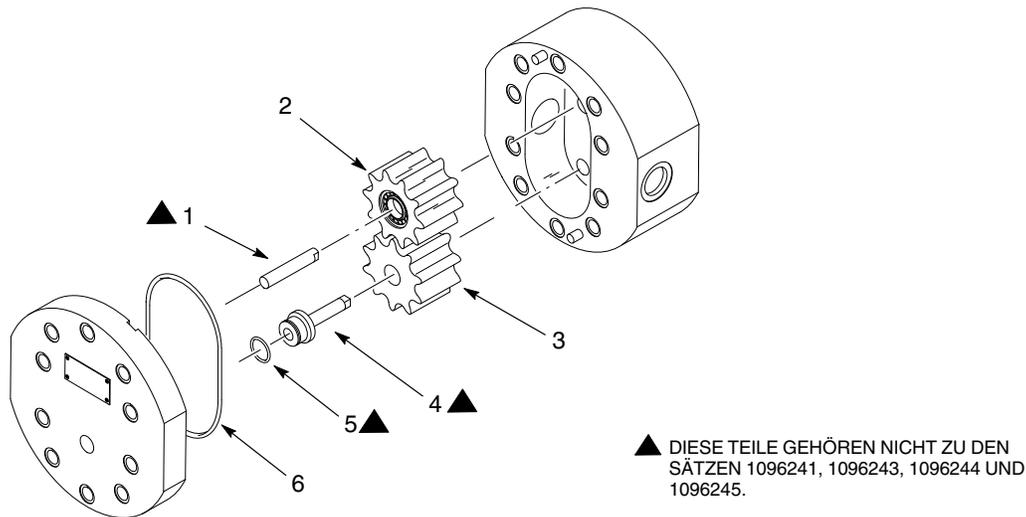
Typischer Durchflussmesser mit eingeschraubter Welle
